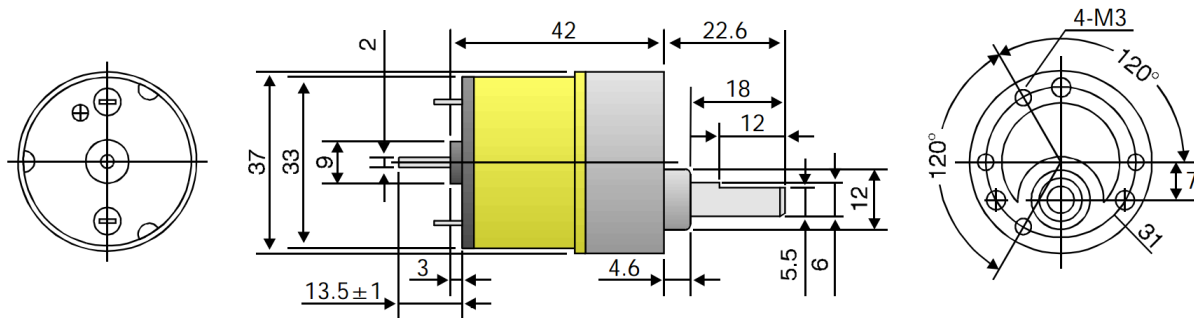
Dimensiones [mm] motor HN-GH7.2-2414T-50:1
